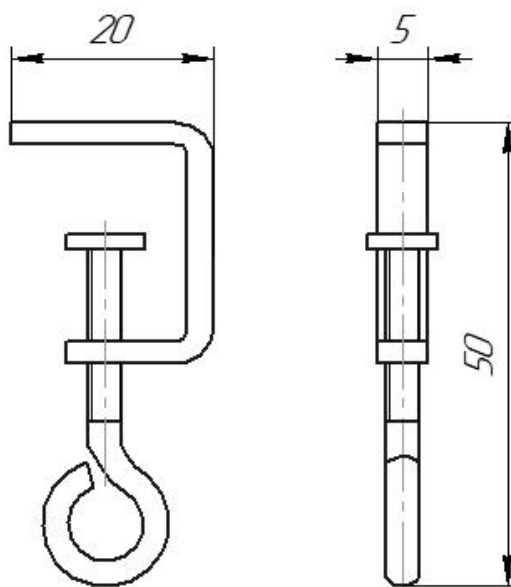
Струбцина для збирання і зварювання проставки корпусу
